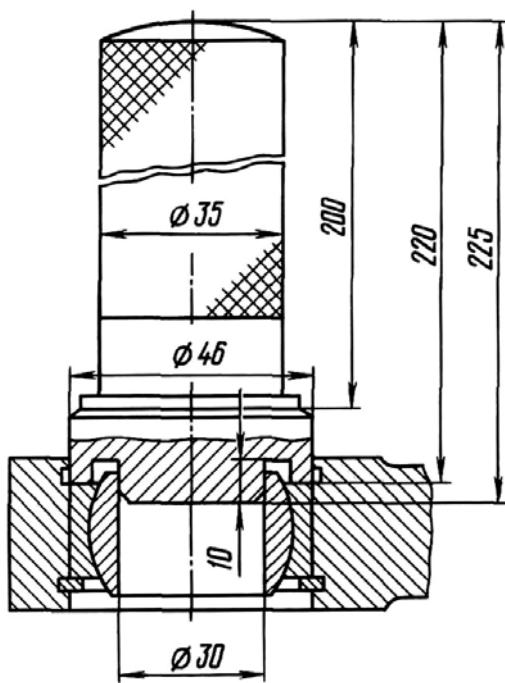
Оправка для запрессовки и выпрессовки шарнирного подшипника
